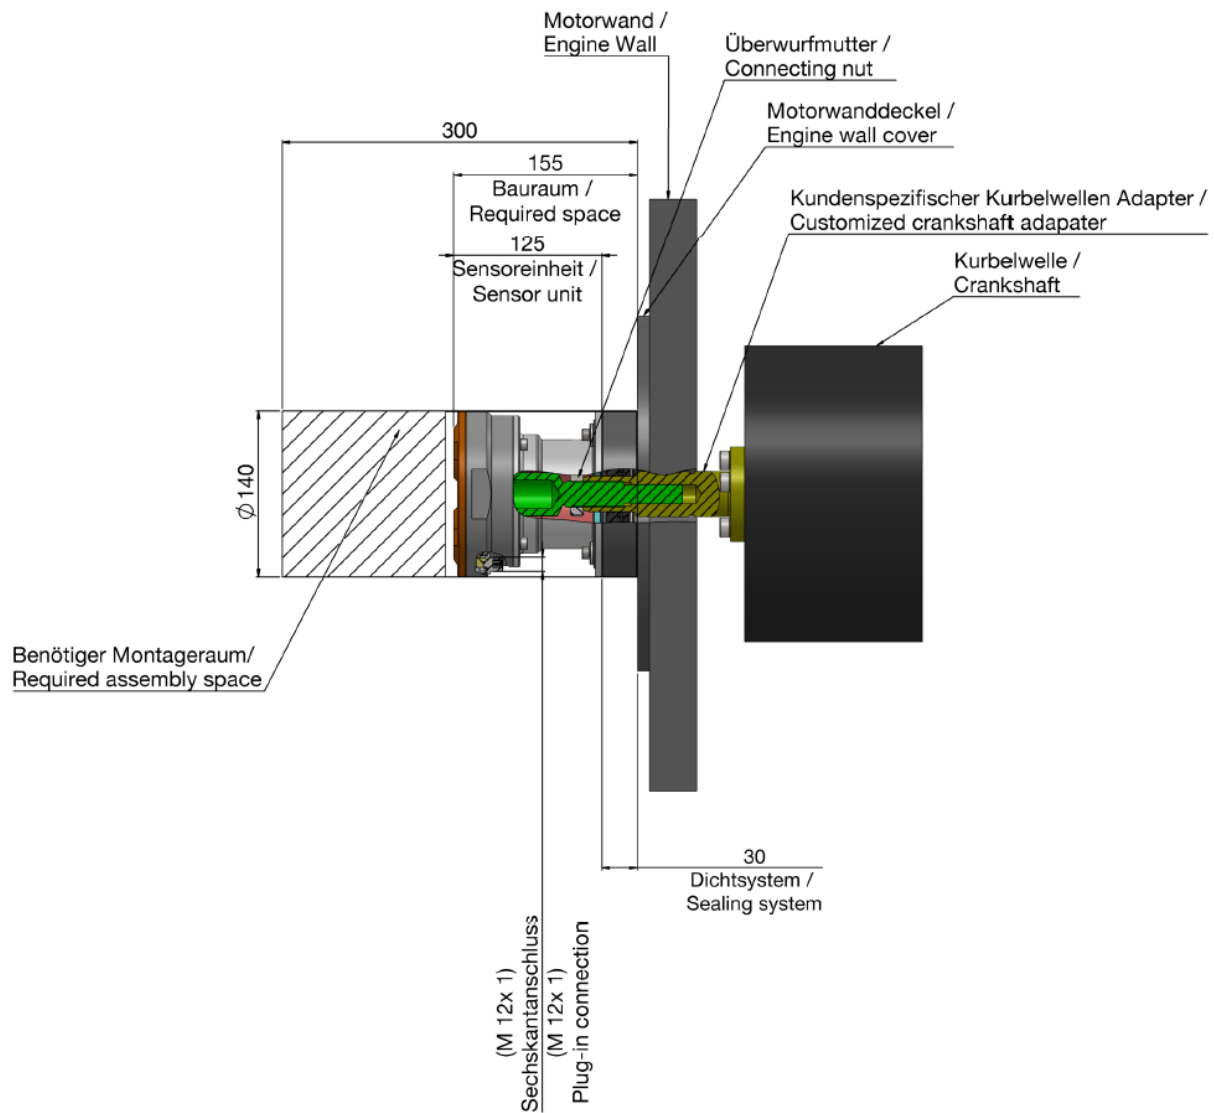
Sensorschnitt - kurz (mit Wellendichtring)
